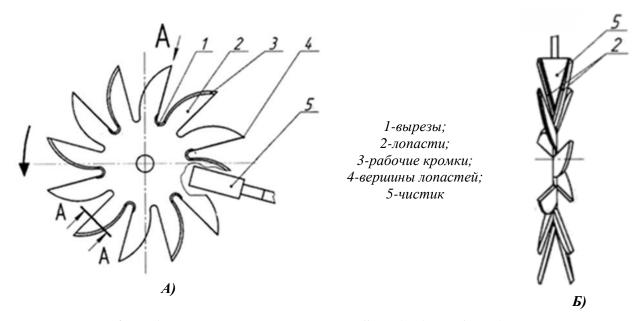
Рабочий орган лопастного типа: А) - вид сбоку; Б) – вид сверху
